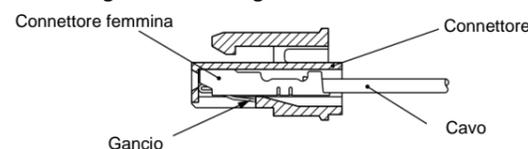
Collegamento e scollegamento dei cavi con connettore femmina
